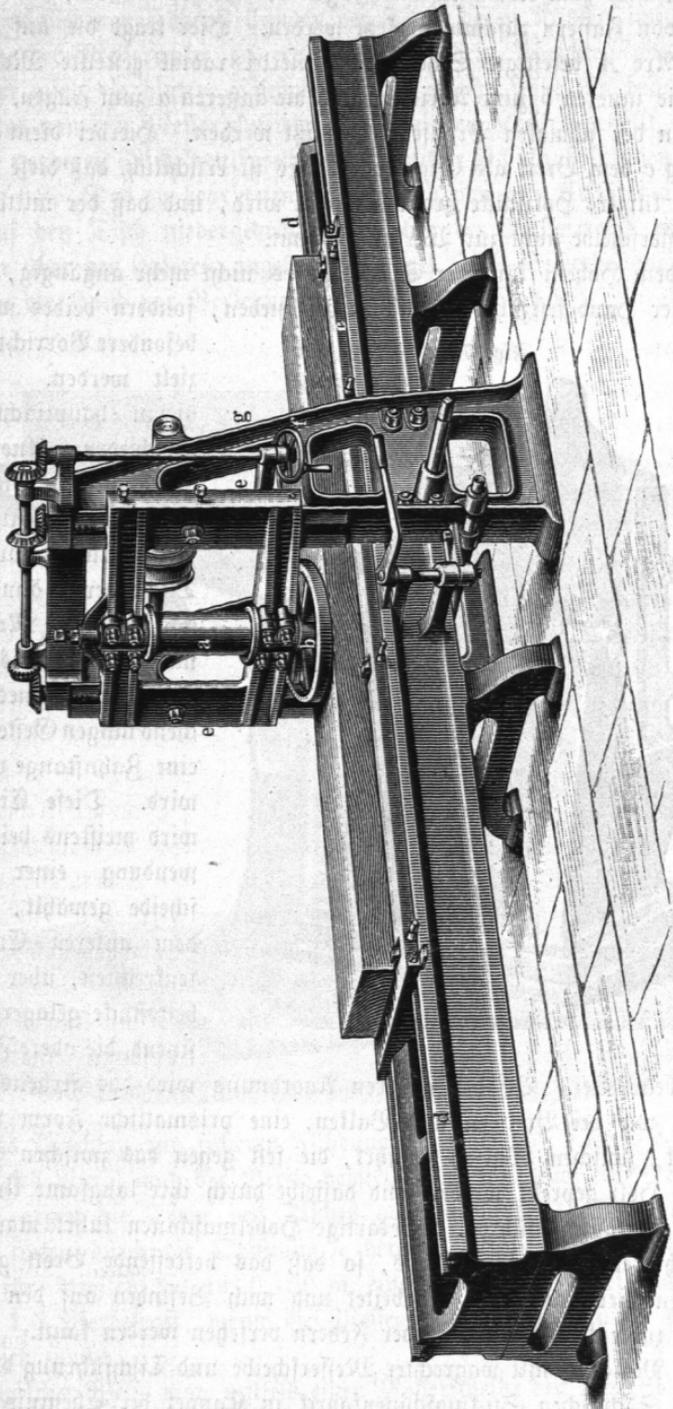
Die Messer ragen aus der unteren Fläche der auf der senkrechten Spindel *a* befestigten Scheibe *b* hervor, die durch einen auf *a* geführten halbgeschränkten Riemen schnell umgedreht wird, während das zu hobelnde Holz auf der Tischplatte *c* durch geeignete Spannvorrichtungen befestigt ist. Wenn diese in den prismatischen Führungen des Bettes *d* geleitete Tischplatte in der von den Metallhobelmaschinen her bekannten, in der Figur nicht näher erläuterten Art langsam verschoben wird, so wird durch die Messer oder stichelförmigen Schneiden der Scheibe *b* die obere Fläche des Holzes in der schon oben besprochenen Weise abgerichtet. Die Messerwelle findet hierbei ihre Lager in einem Rahmen *e*, der an den senkrechten Führungsbahnen des Gestelles *g* mittelst der beiderseits angebrachten Schraubenspindeln durch Umdrehung des Handrades *f* sehr genau verstellt werden kann, so daß man hierdurch nicht nur die Stärke des abzunehmenden Spanes in der Hand hat, sondern auch den jeweiligen Dicken verschiedener Hölzer entsprechend die Stellung der Messerscheibe bestimmen kann.
